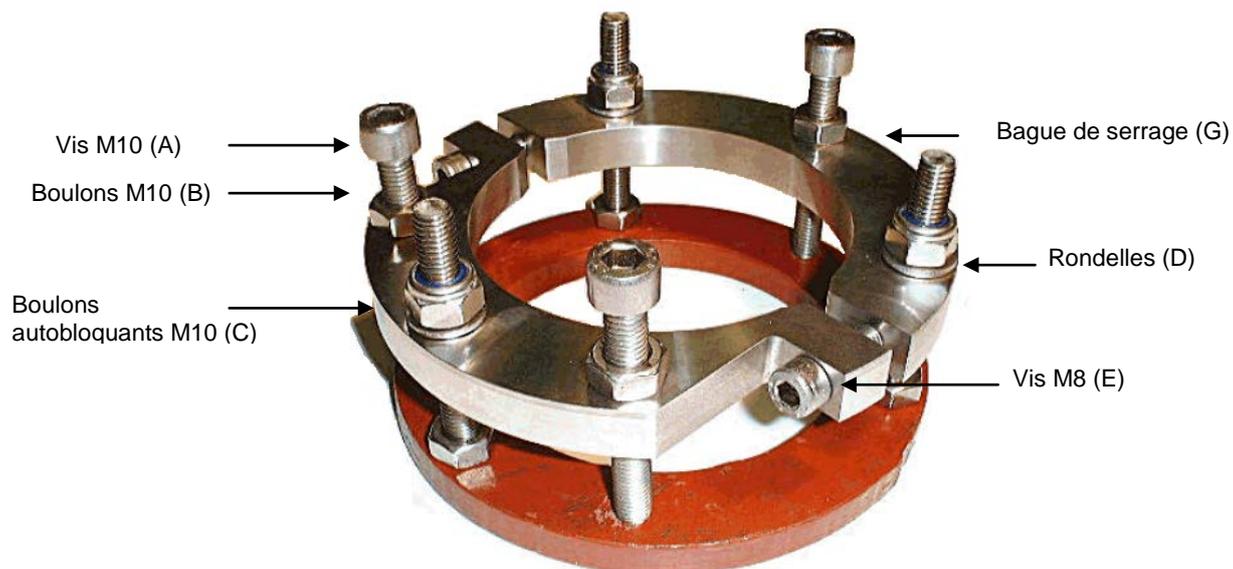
bague de serrage universelle assemblée et installée sur la plaque de fixation
